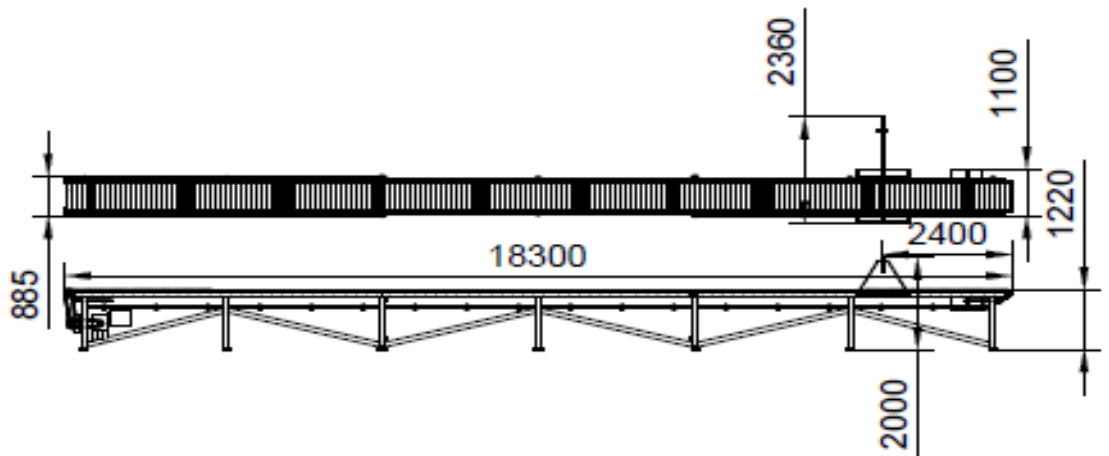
Габаритные размеры. Пластинчатый конвейер.
